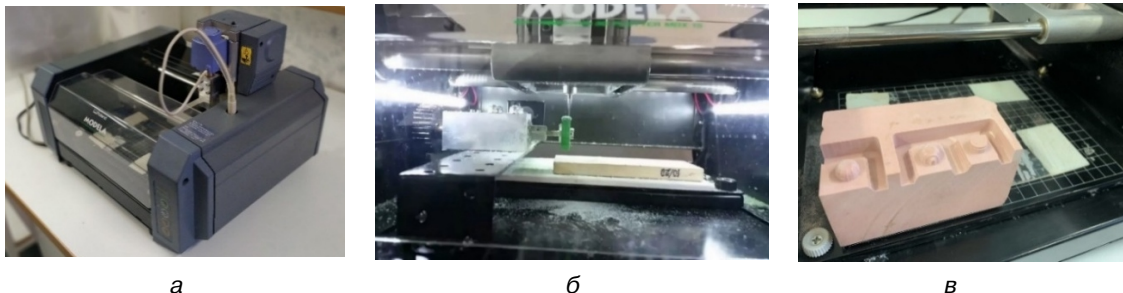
Фрезерный станок Roland MDX-20: а — общий вид; б, в — рабочая зона обработки
